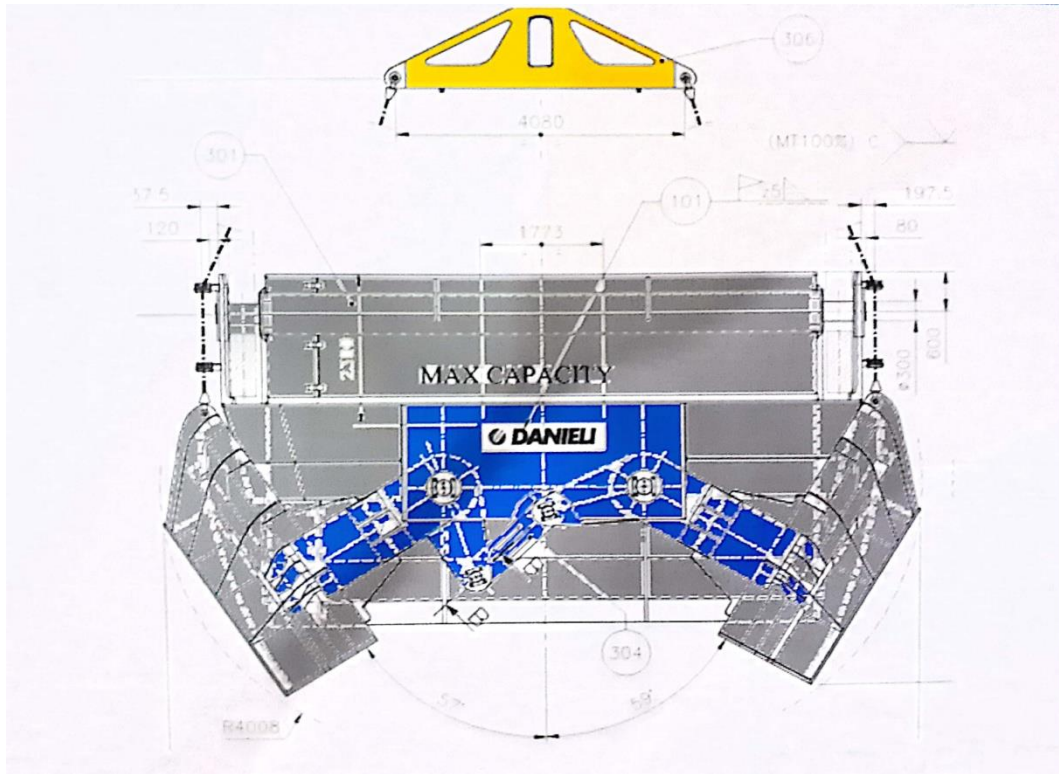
Dispositif d'ouverture du panier à ferrailles
